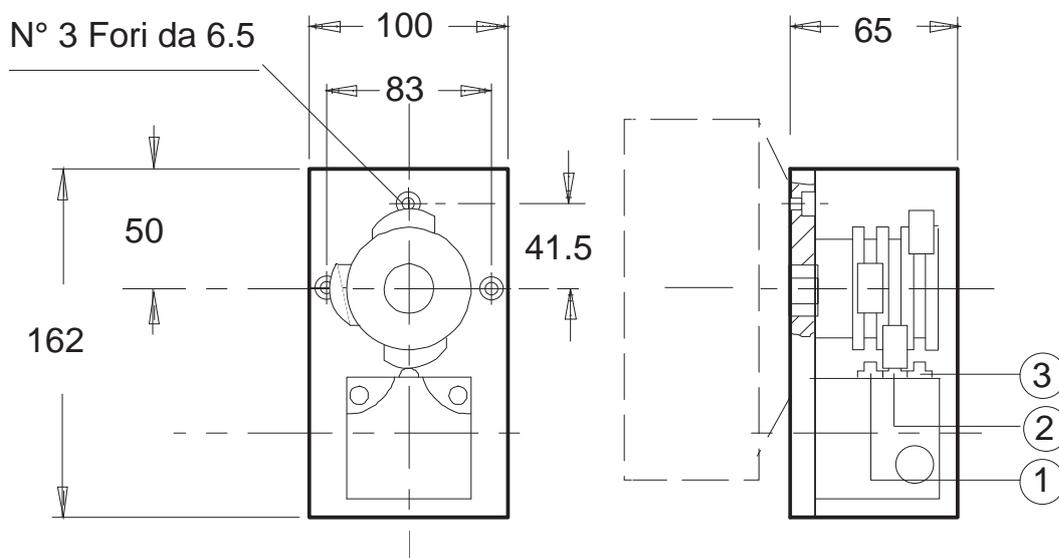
Dimensioni di ingombro del gruppo completo FC3.
